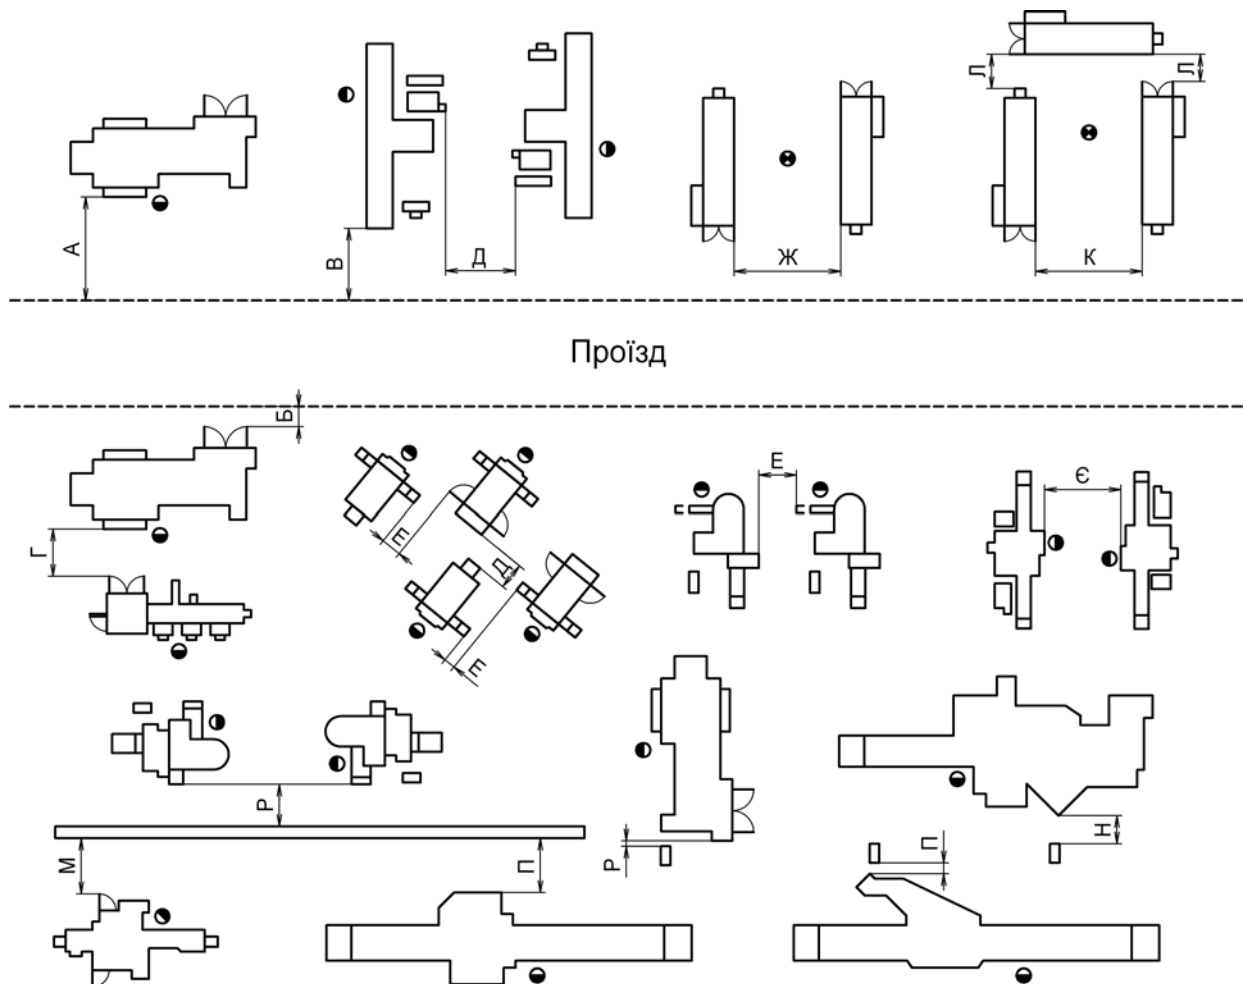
Варіанти розташування верстатів відносно один одного, корпусного проїзду, стін і колон корпусу:
